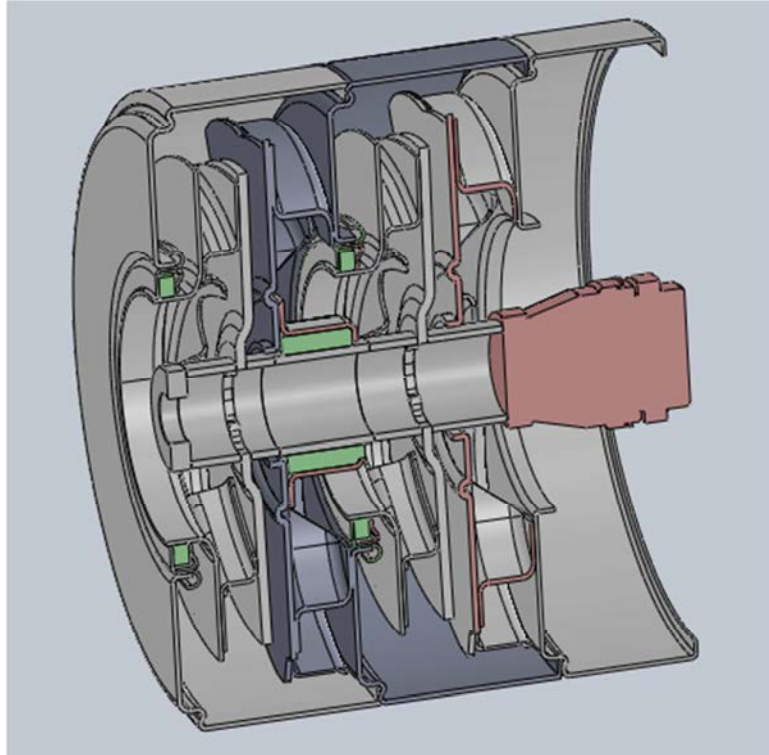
Vista in prospettiva MXV\_65 con sezione nel piano meridiano.
